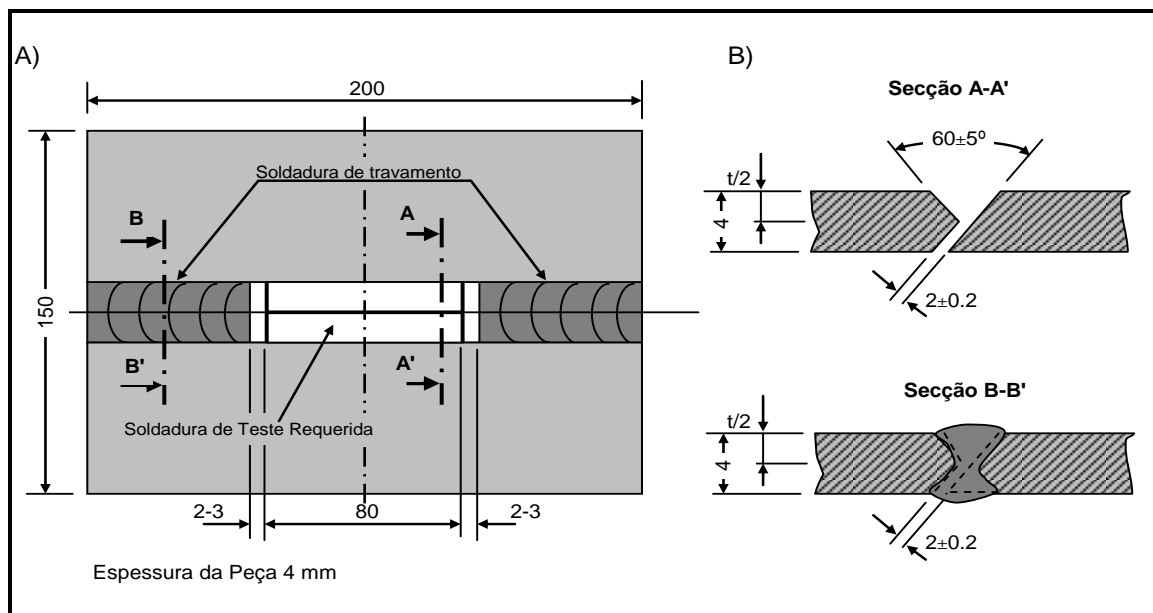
Ilustração Esquemática do Ensaio Tekken: A) Vista da Peça; B) Preparação de Soldadura de Teste e soldadura de travamento.
